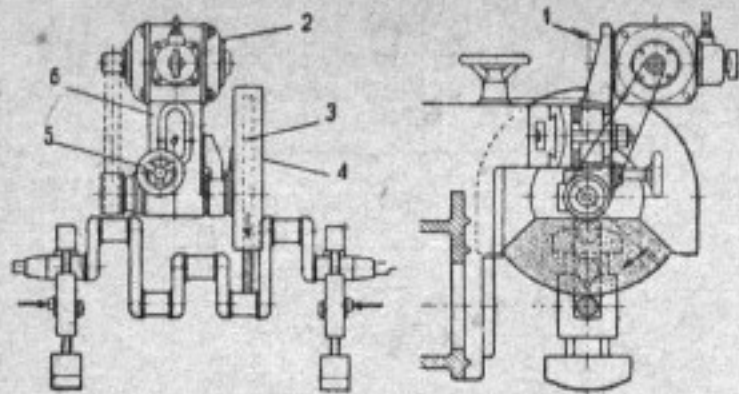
Суппортный шлифовальный прибор для шеек коленчатого вала
